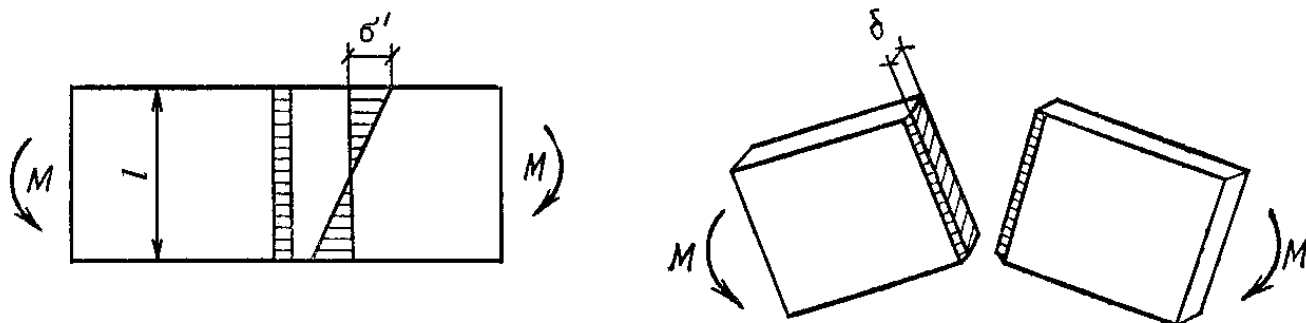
Схема нагружения стыкового сварного шва моментом M
